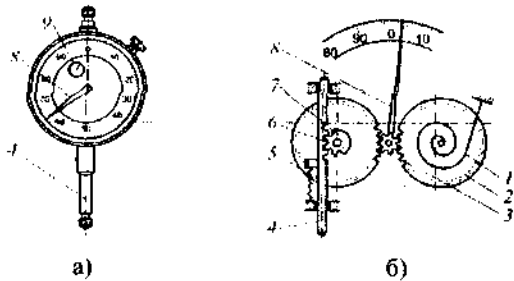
Индикатор часового типа (а) и его схема (б): 1 – спиральная пружина; 2, 3, 5 и 7 – зубчатое колесо; 4 – стержень; 6 – зубчатая рейка; 8 и 9 – стрелка
